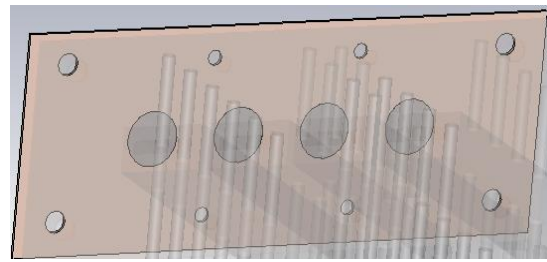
69 Detalle de los parches apilados de los elementos radiantes
